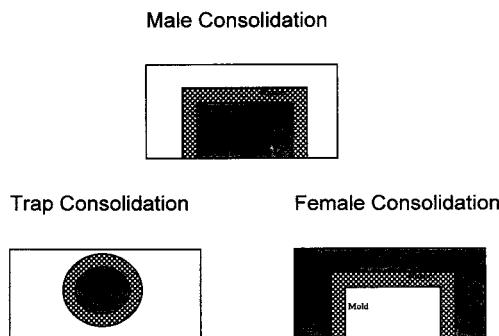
Rubber tool configuration : ■ Rubber tool, □ Prepreg, □ Mold.
